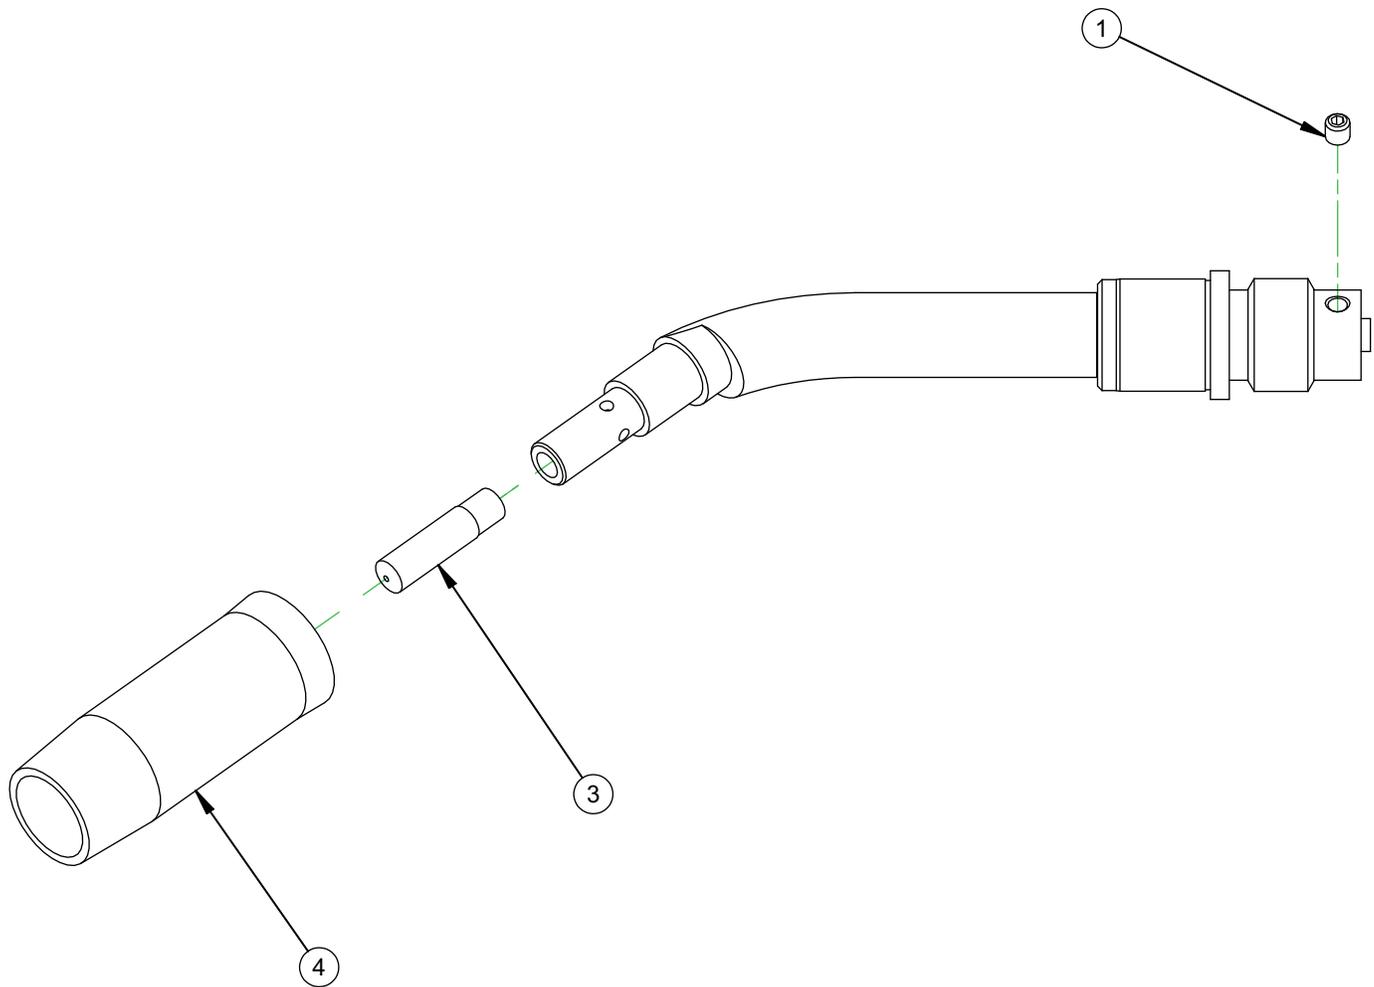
ENSEMBLE TORCHE À VERGE POUR DIAMÈTRE EXTÉRIEUR (RÉF. 81384)
